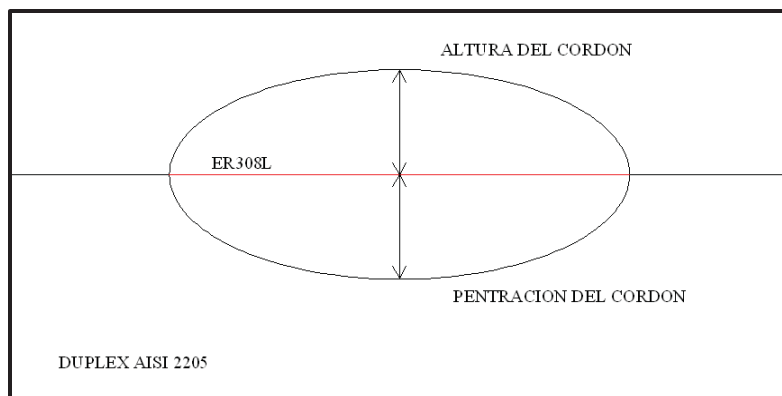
2 Forma de medición de altura y penetración del cordón de soldadura.
